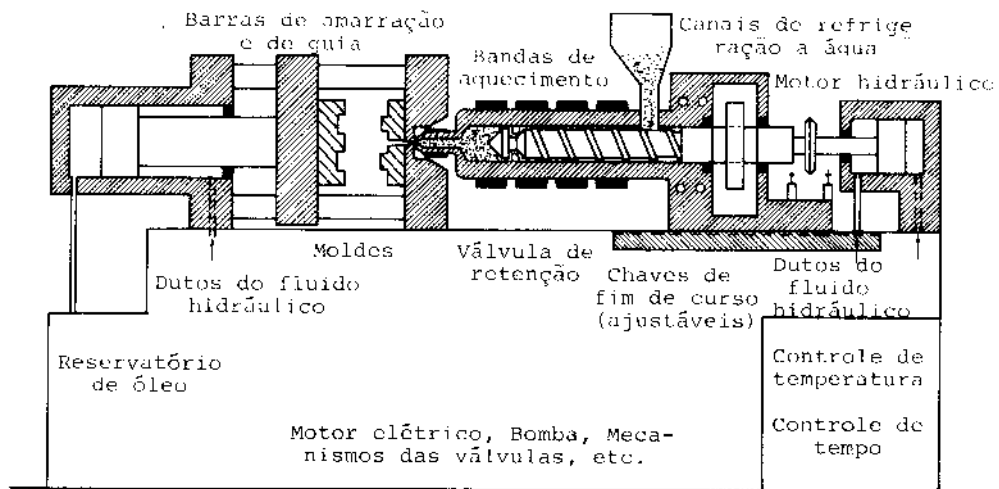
Máquina de moldagem por injeção de parafuso simples. Figura originalmente apresentada em Blass (1985).
